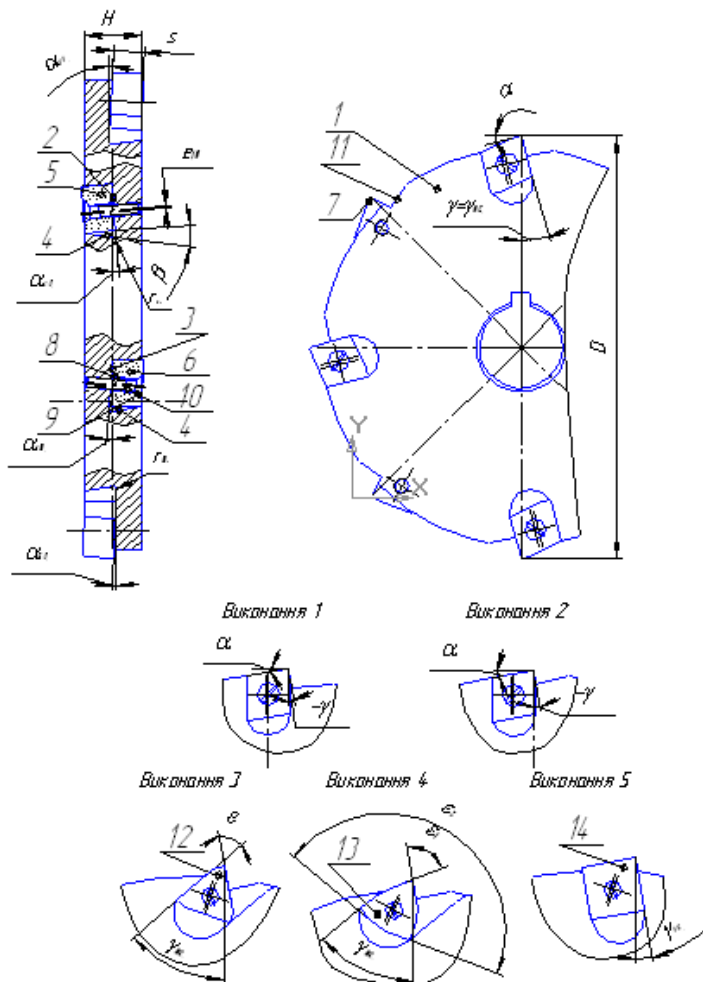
Предлагаемая конструкция сборной дисковой отрезной фрезы и варианты оснащения ее МНП боковой установки
